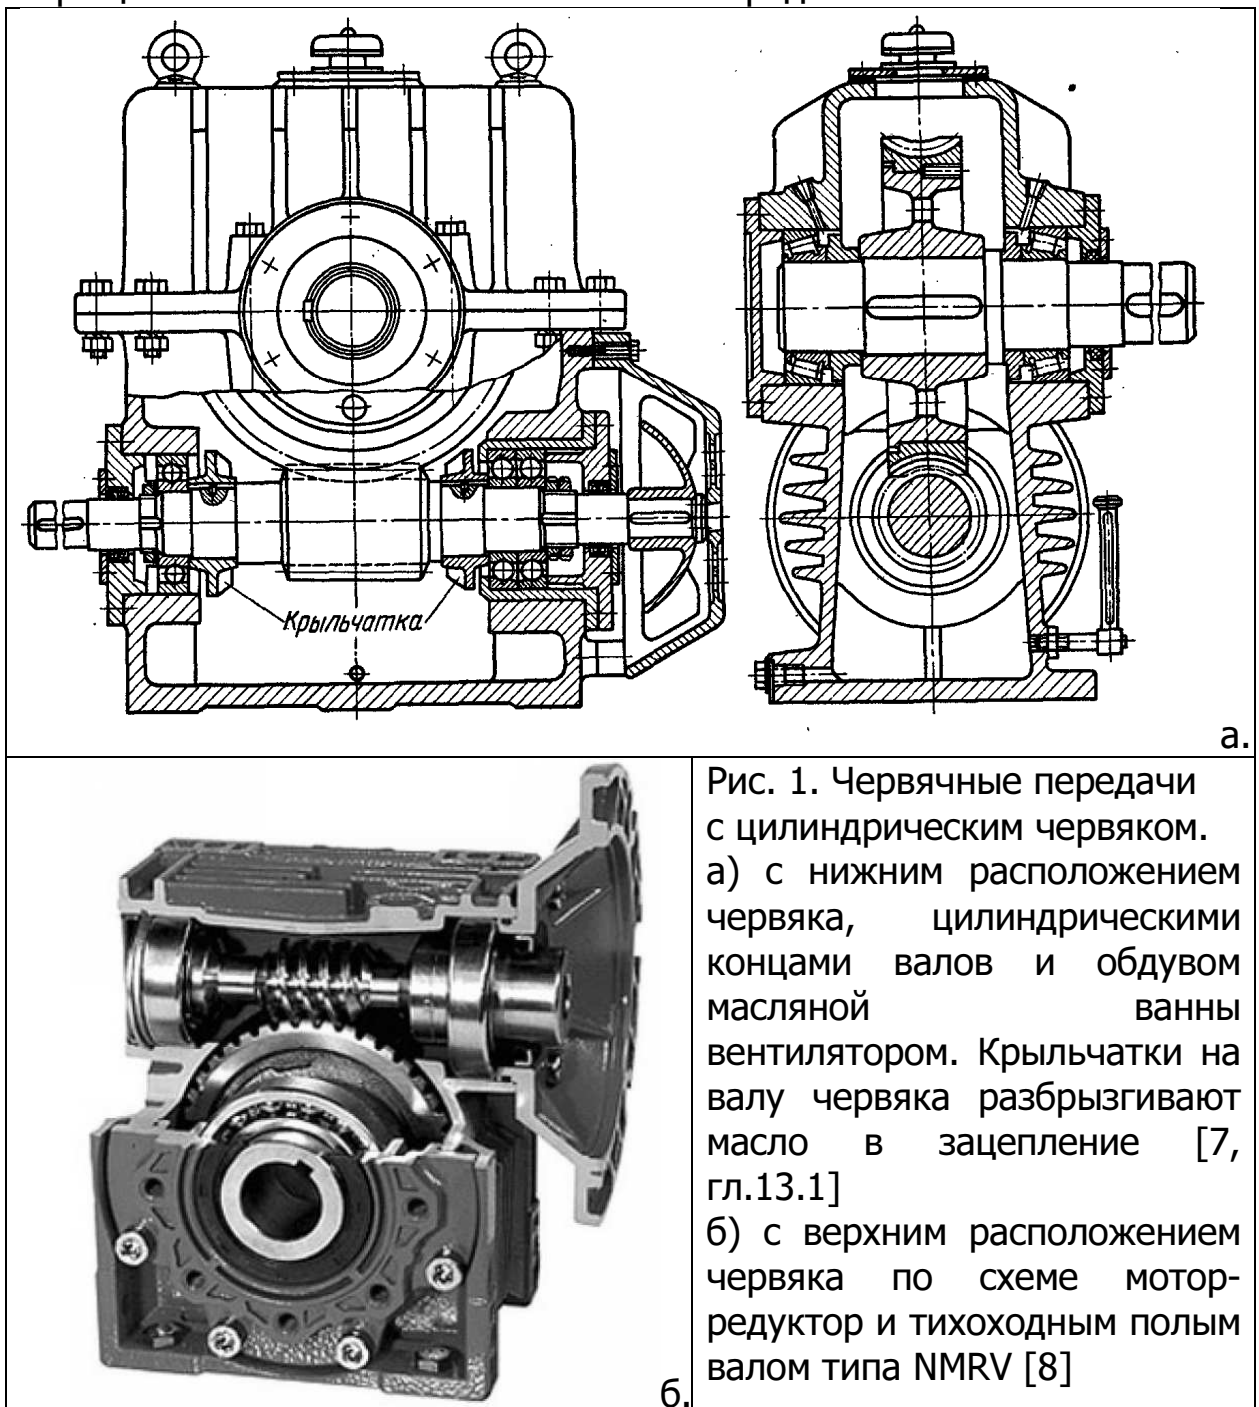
Червячные передачи с цилиндрическим червяком. а) с нижним расположением червяка, цилиндрическими концами валов и обдувом масляной ванны вентилятором. Крыльчатки на валу червяка разбрызгивают масло в зацепление [7, гл.13.1] б) с верхним расположением червяка по схеме мотор-редуктор и тихоходным полым валом типа NMRV [8]
